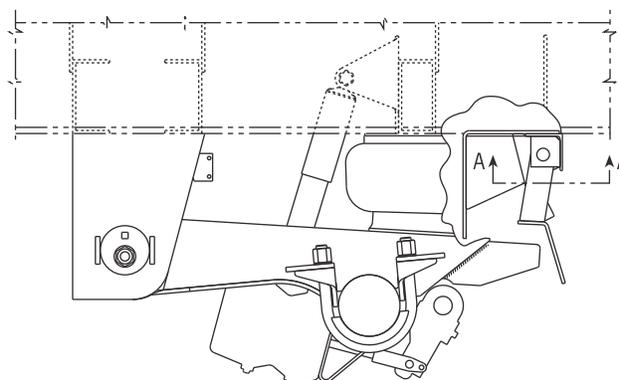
Detalles de soldadura del Kit SLKQ
